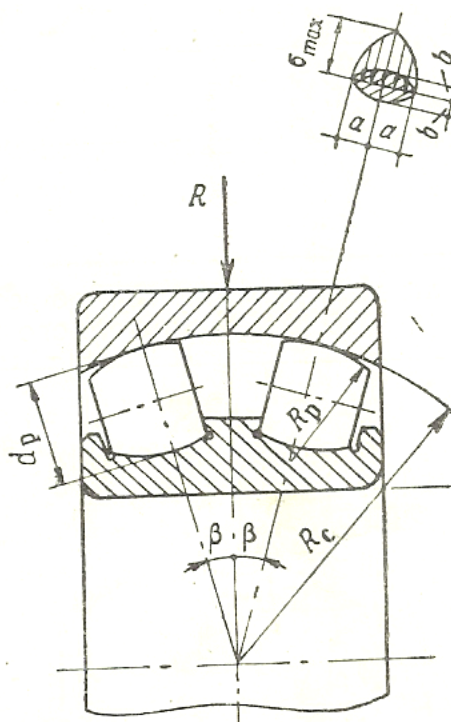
Подшипник роликовый радиальный сферический двухрядный
